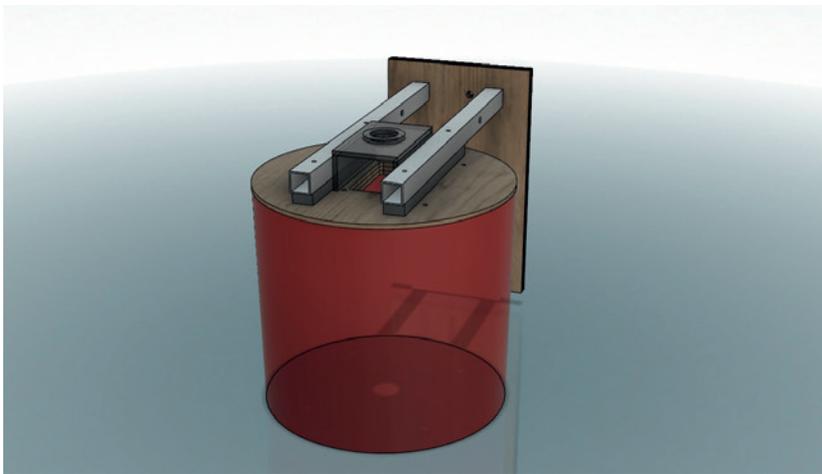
Malzmühle elektrifiziert: Die Mühle kommt in das durchsichtige Gehäuse, obendrauf wird ein Trichter und hinten dran ein Mörtelmixermotor platziert. Im roten Eimer landet das geschrotete Malz.
